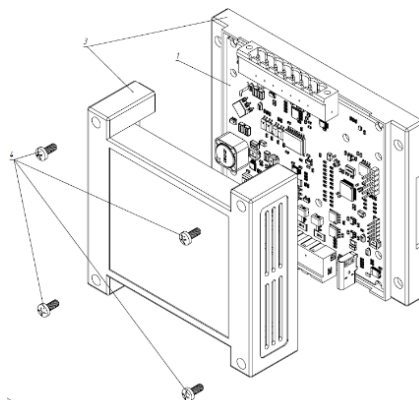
Разнесенная сборка нормирующего преобразователя для термопар: 1 – печатная плата; 2 – корпус; 3 – крепежные винты
